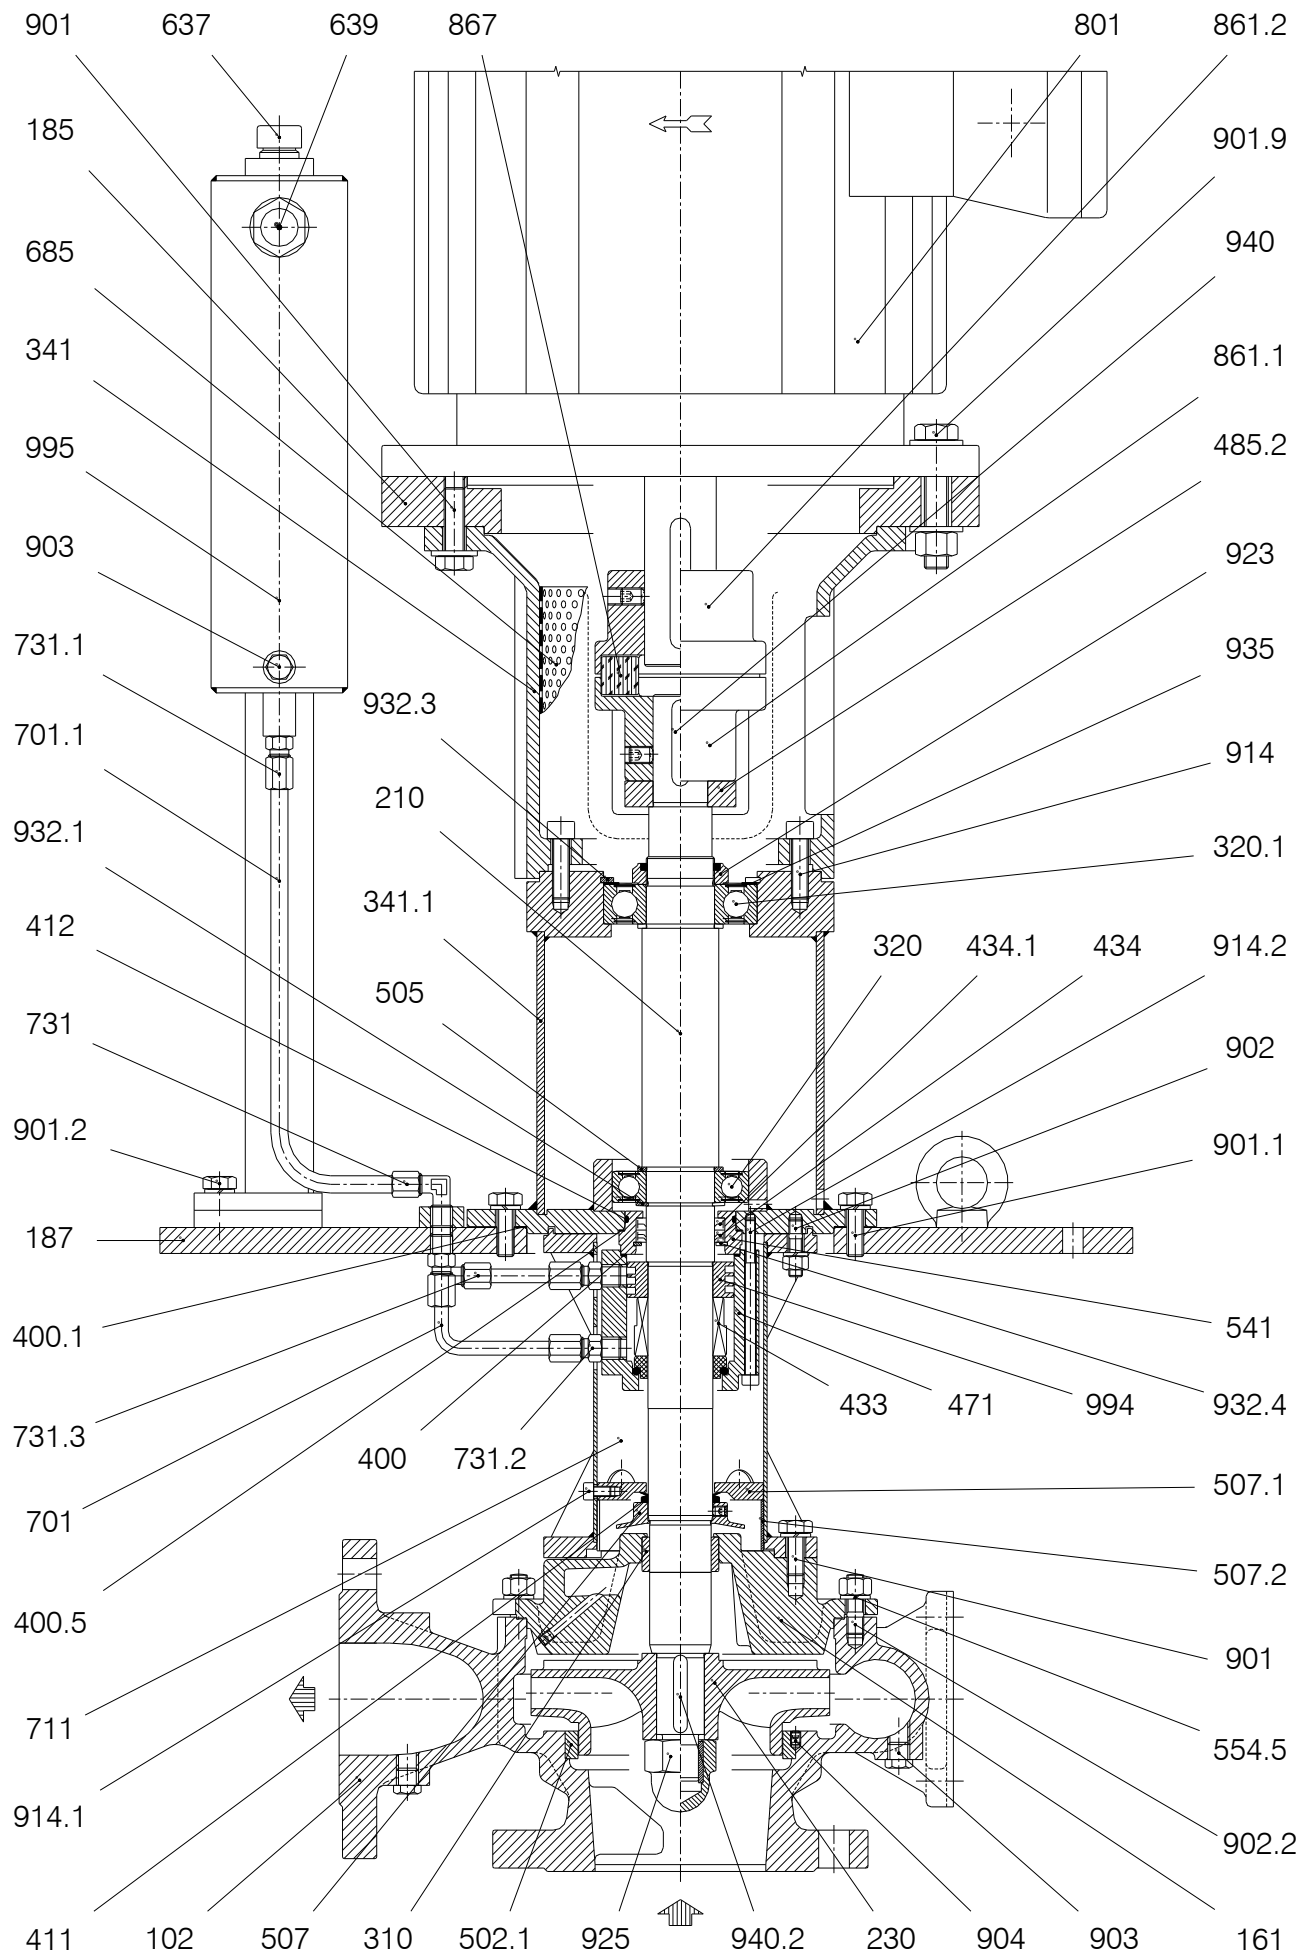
Pumpe der Baureihe TCHV in Ausführung /1-R = mit einfacher mechanischer Abdichtung
